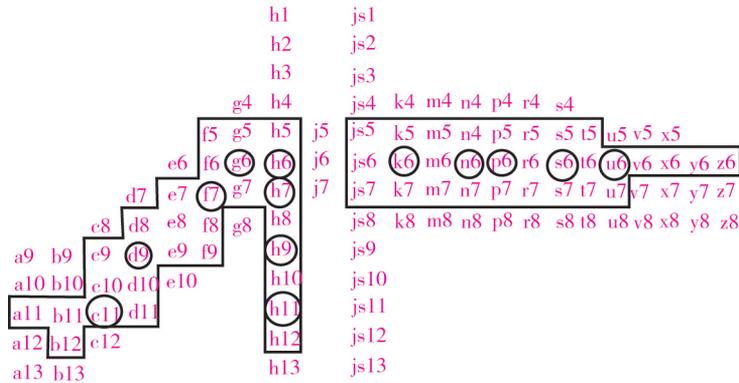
轴的一般、常用和优先公差带（尺寸 ≤ 500 mm）
